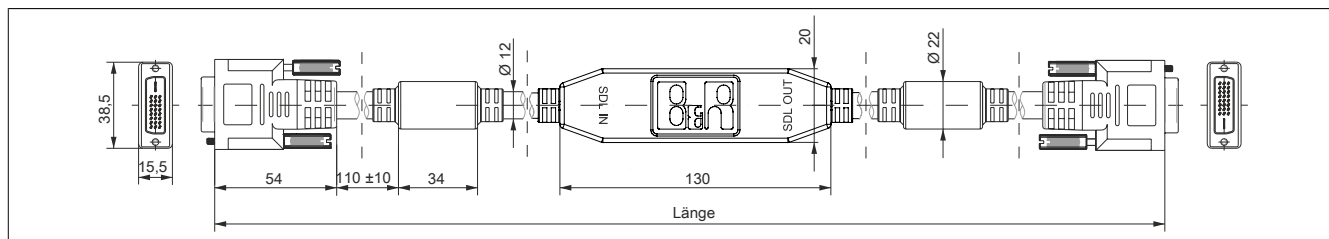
5CASDL.xxxx-13 ≥ Rev. E0 - Abmessungen
